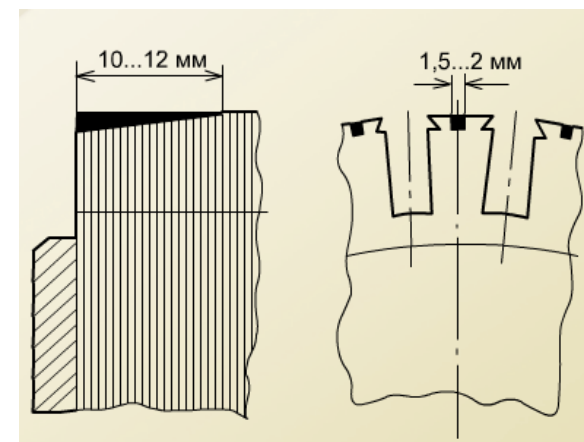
Ремонт сердечника з розпушеними крайніми пакетами шляхом зварки
